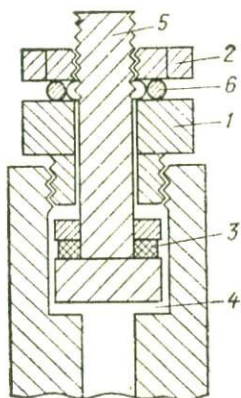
Схема устройства, позволяющего вытаскивать обтюратор из автоклава:
